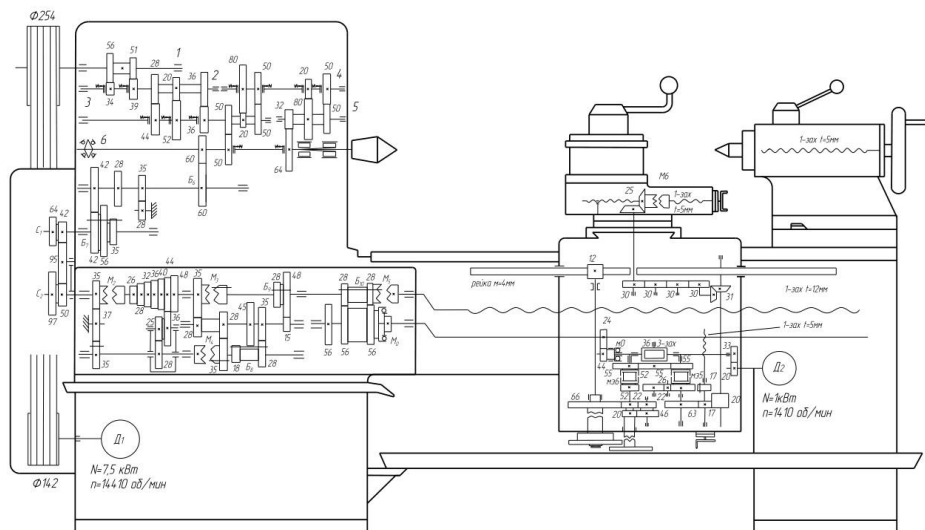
Кінематична схема приводу головного руху токарно-гвинторізного верстата.
